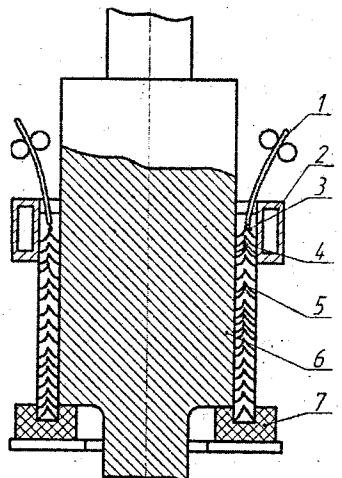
Схема електрошлакового наплавлення циліндричної поверхні:
